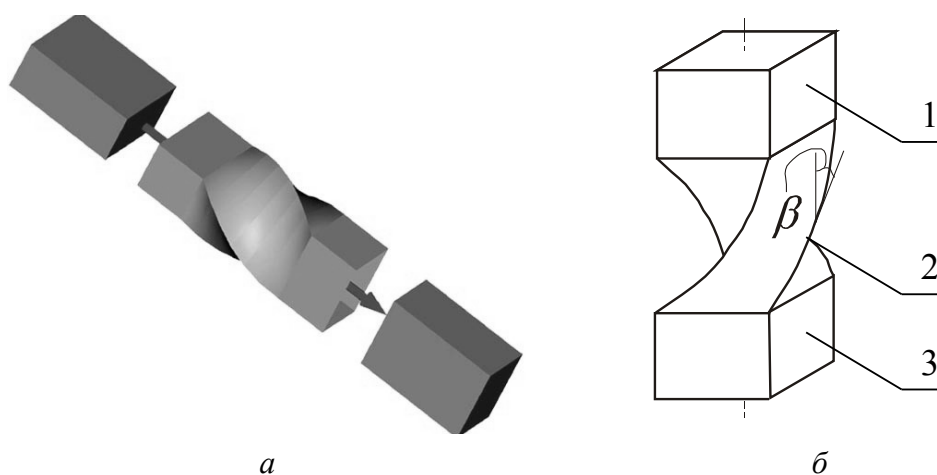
Схема, поясняющая суть винтовой экструзии: а – схема прохождения заготовки через винтовую матрицу; б – схема канала винтовой матрицы
